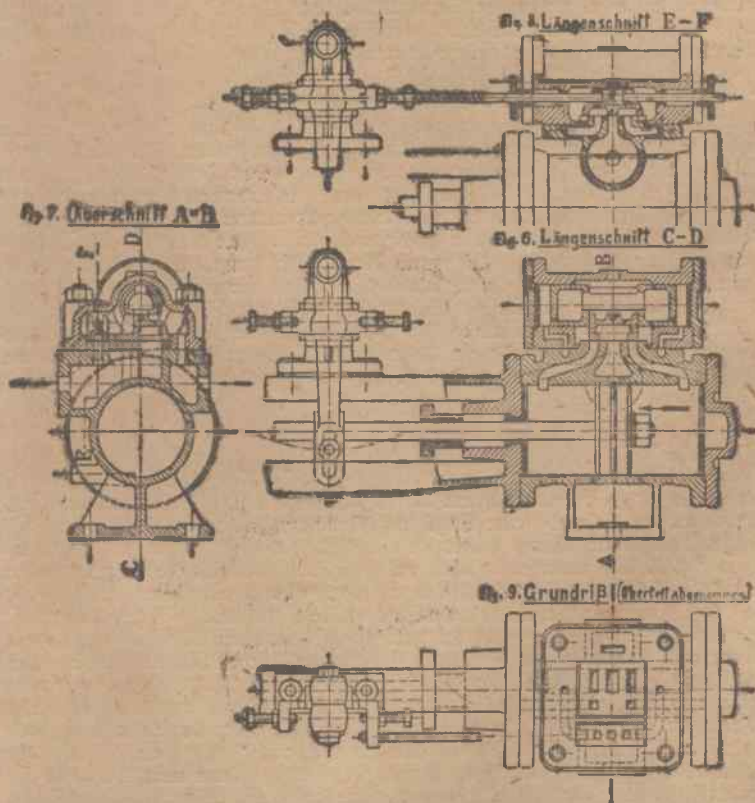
bis 9 Dampfcylinder einer schwinggradlosen Dampfmaschine.
